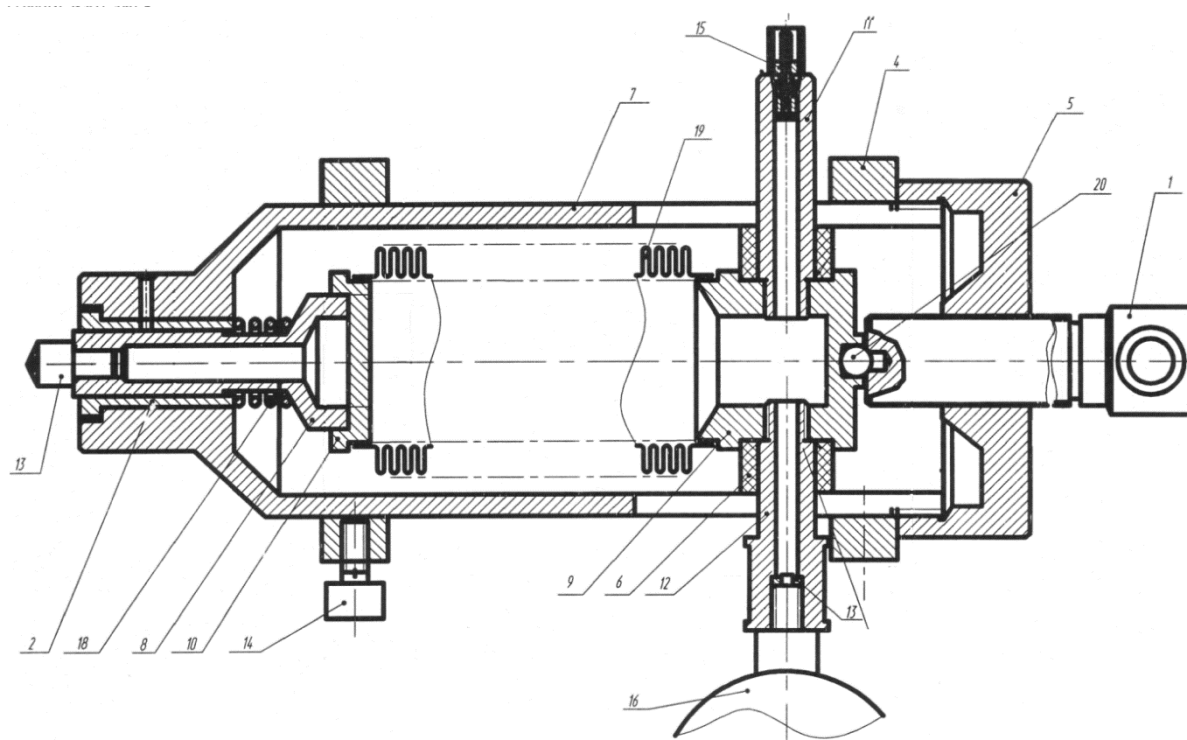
Чертеж оправки с пневматической пружиной.
